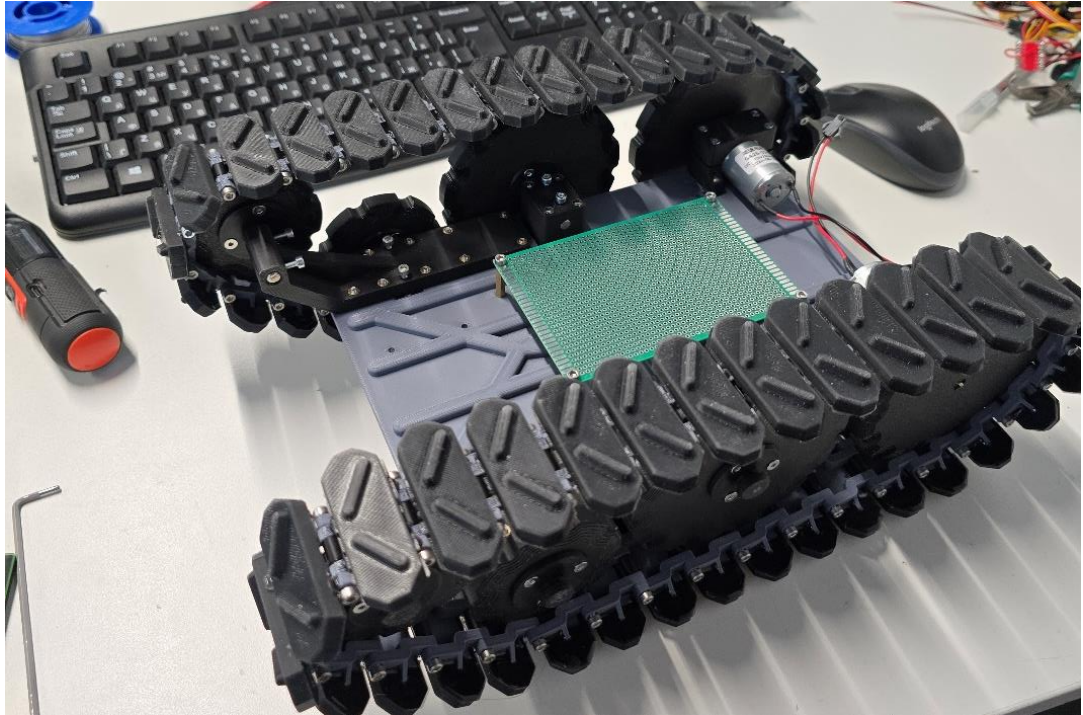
Зовнішній вигляд механічної частини РП
